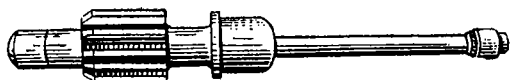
Оправка О-141 для проверки установки вала масляного насоса и центровки ведомого диска при монтаже сцепления
